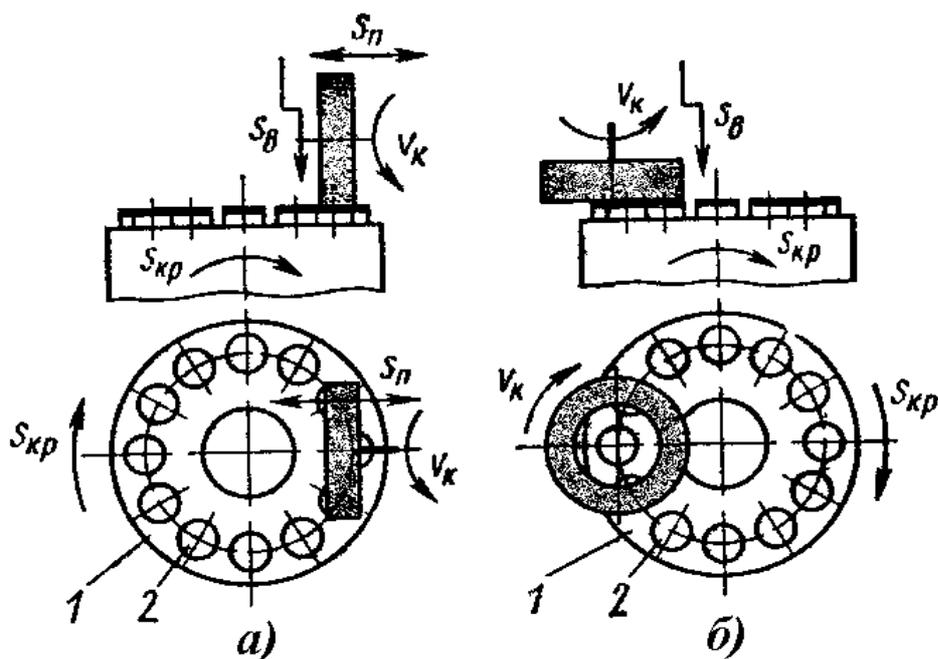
Схемы непрерывной обработки заготовок на плоско-шлифовальных станках с круглым столом:
